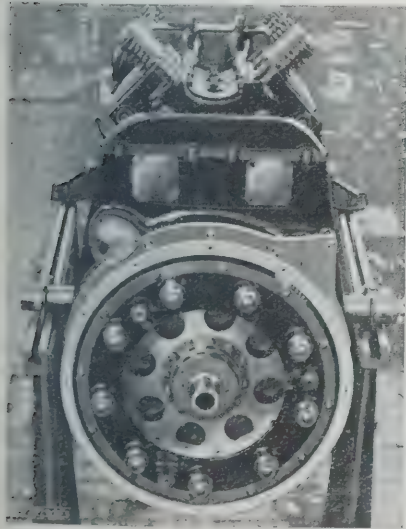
und 4. Sechszylindermotor von 110/130 mm der Maudslay Motor Co.
